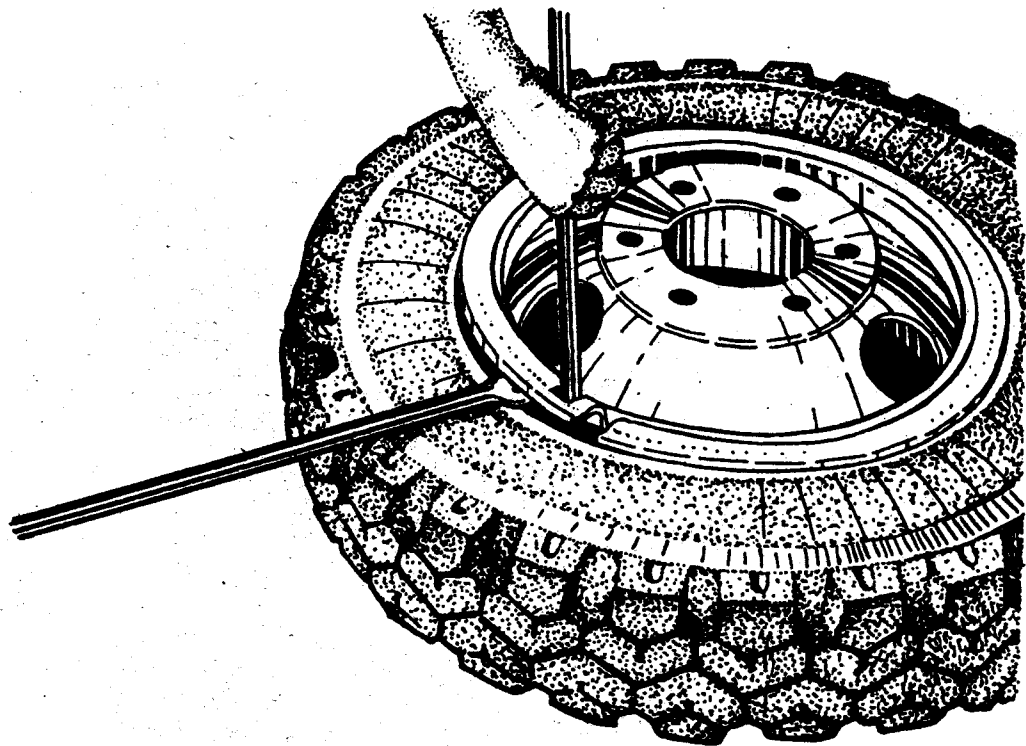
Установка прямой лопатки в прорезь бортового кольца
